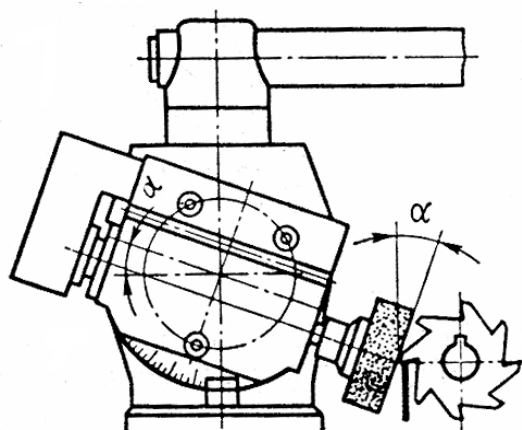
Шлифовальная бабка станка мод. 3М642
